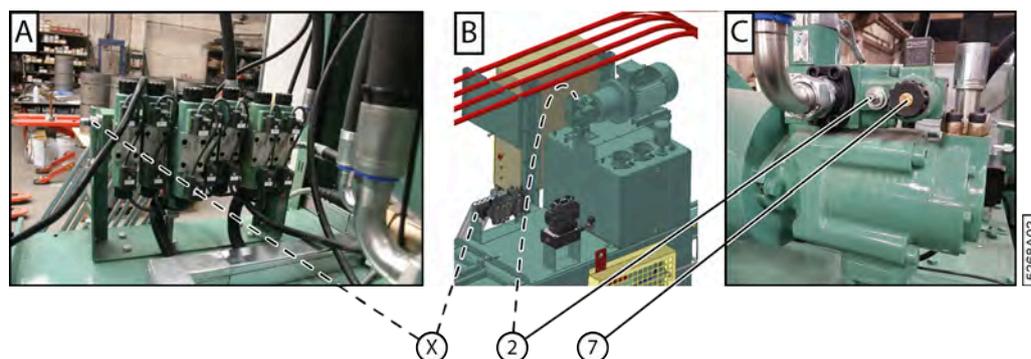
Vue de gauche [A], vue de face à gauche [B] et vue de droite [C]
